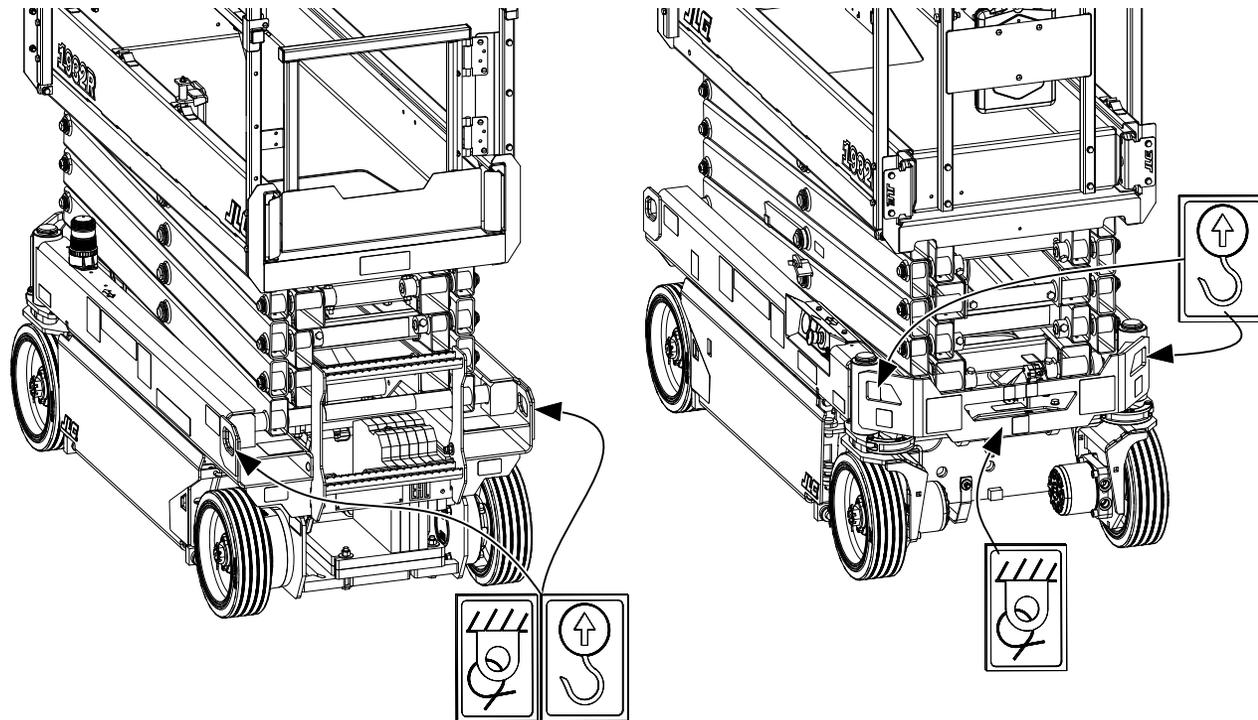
Localização dos Olhais de Amarração e Elevação
